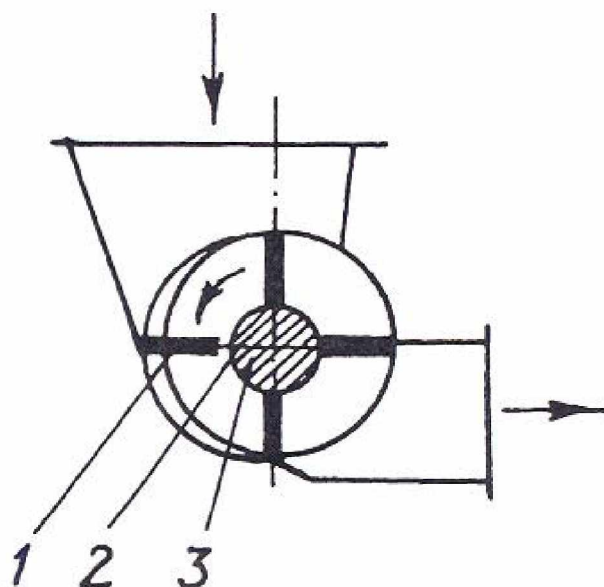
Лопатевий дозатор: 1 – шибер; 2 – ротор; 3 – вал ротора.
